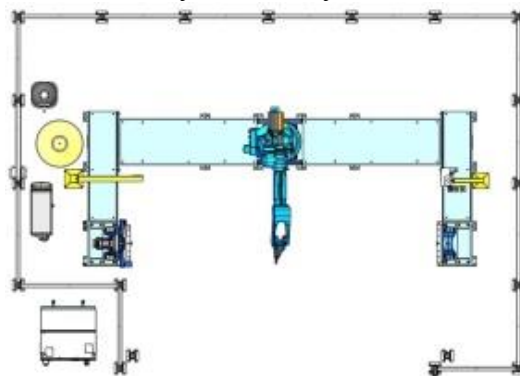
Компоновочный чертеж компактной сборочно-сварочной системы
